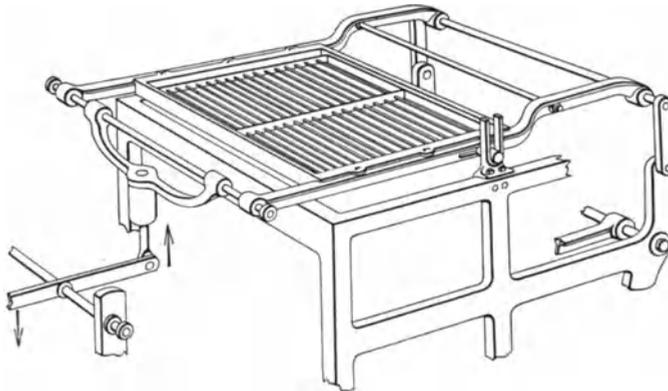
Schema einer Messerkastenbewegung für Schrägfach.
